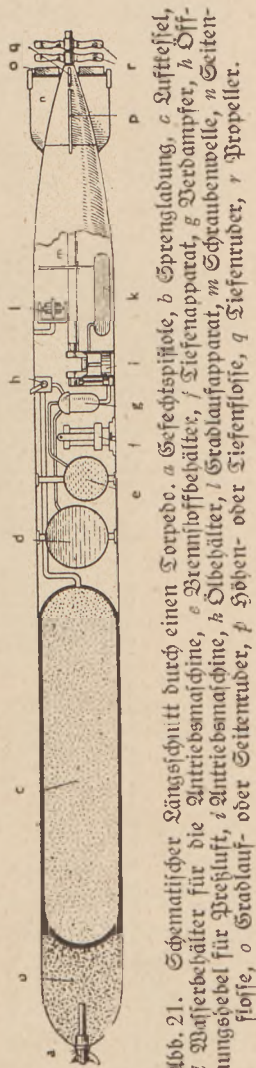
Schematischer Längsschnitt durch einen Torpedo. a Gesichtspistole, b Sprengladung, c Luftkessel, d Wasserbehälter für die Antriebsmaschine, e Bremsstoffbehälter, f Tiefenapparat, g Verdampfer, h Öffnungsgebel für Preßluft, i Antriebsmaschine, k Schraubenwelle, l Seitenruder, m Höhen- oder Tiefenflöße, n Tiefenruder, o Propeller.
